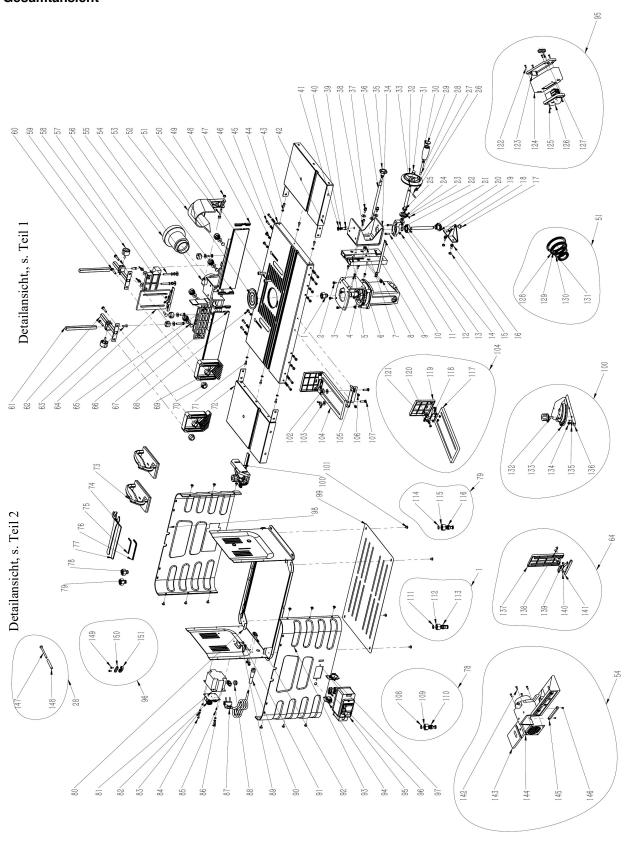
Ersatzteilzeichnung Tischfräse TF 50 E - Gesamtansicht
